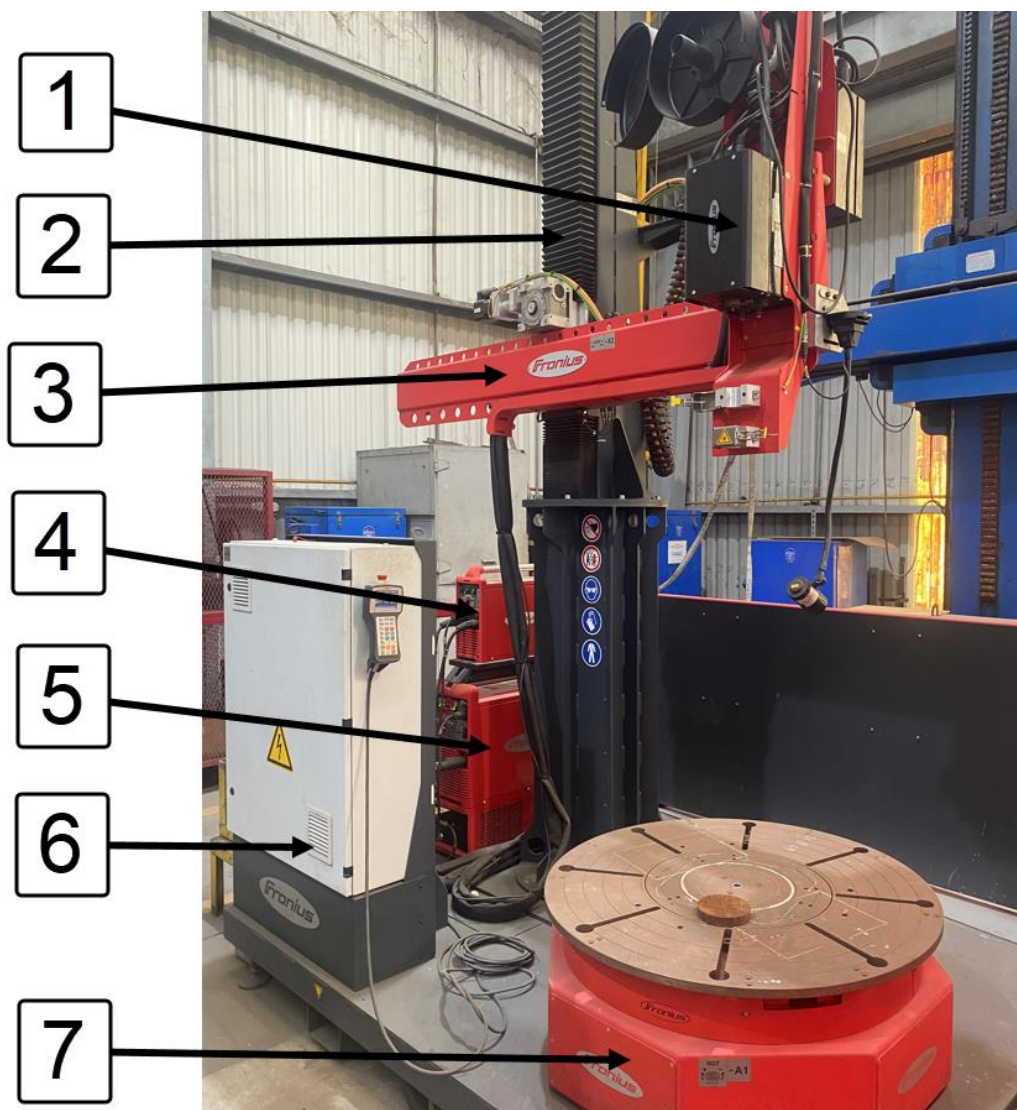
Foto do equipamento de revestimento de soldagem mecanizado CCC (compact cladding cell). Angulo 1.
